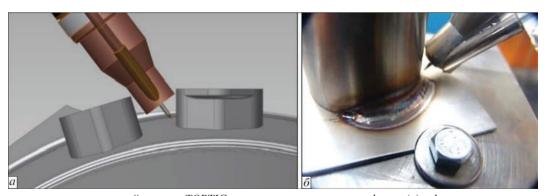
Схема размещения сварочной горелки TOPTIG между привариваемыми муфтами (a) и фрагмент сварного шва модельного элемента, выполненного горелкой TOPTIG (б)
